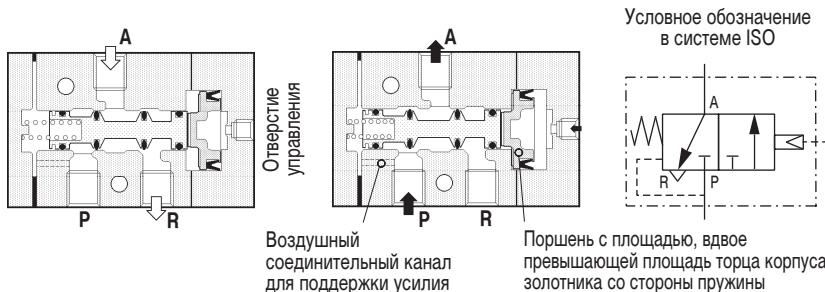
3/2-пневмораспределитель с пружинным и пневматическим возвратом
